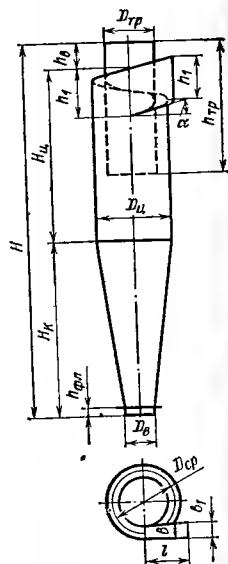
Цилиндрический циклон конструкции НИИОГа
